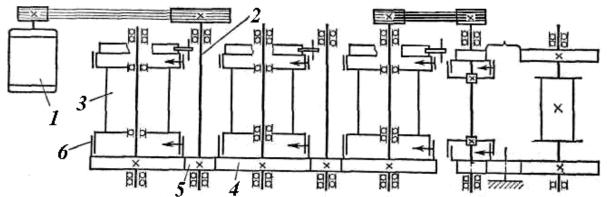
Кинематическая схема многобарабанной фрикционной лебедки: *1* – двигатель; *2* – промежуточный вал; *3* – барабан; *4* – зубчатое колесо второго барабана; *5* – ведущая шестерня промежуточного вала; *6* – ленточный фрикцион
